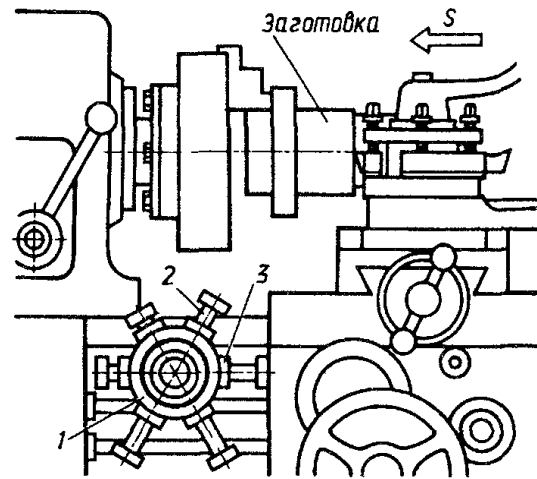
Схема закріплення барабанного упора: 1 - барабанний упор; 2 - упорний гвинт; 3 - контргайка
